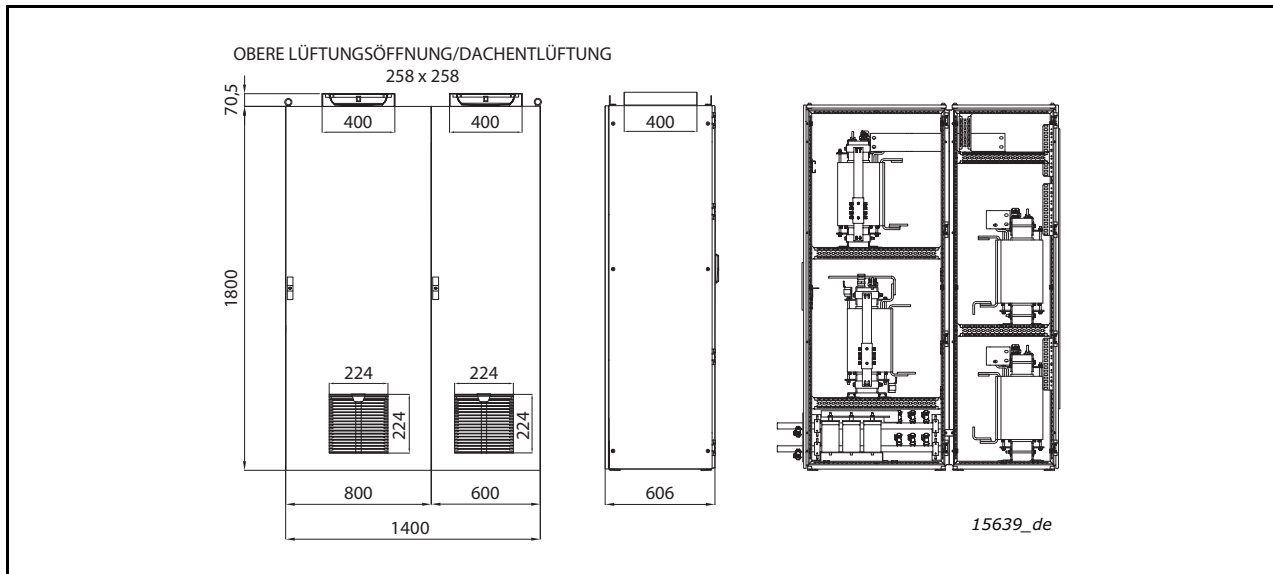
Layout des RLC 1180/1640/2300 A bei Installation in einem Gehäuse
